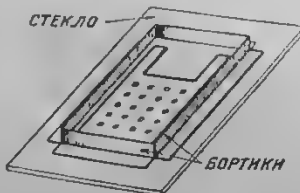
Коробка, служащая для изготовления второй половины формы.
